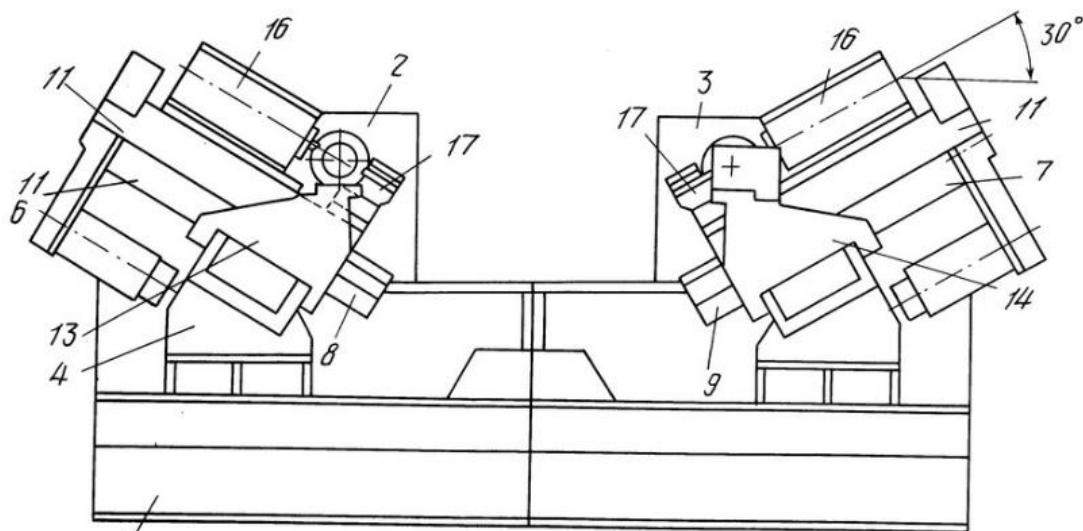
Двошпиндельний токарний верстат по патенту РФ № 2087264
